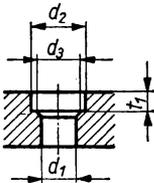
Senkung nach TGL 0-75 für Zylinderschrauben
